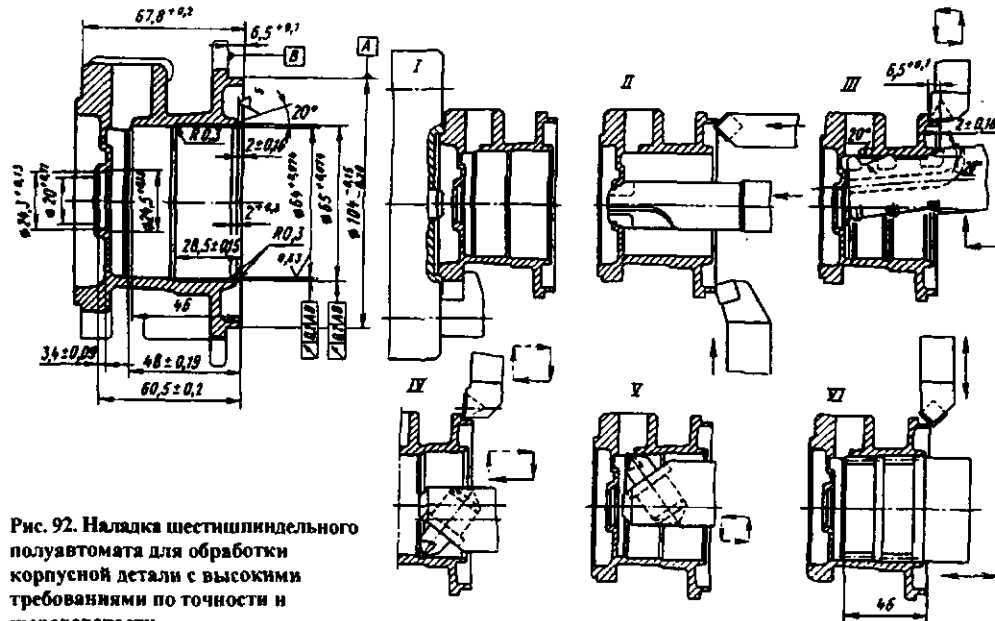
Наладка шестишпиндельного полуавтомата для обработки корпусной детали с высокими требованиями по точности и шероховатости
